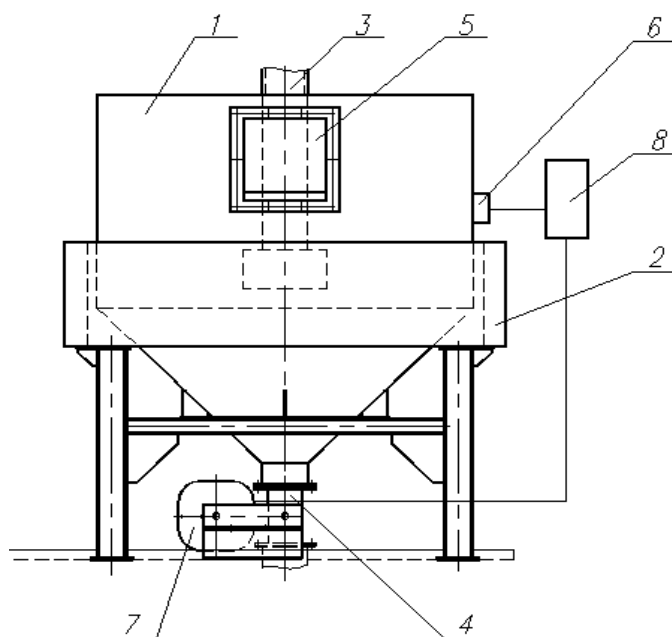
Общий вид магнитно-гравитационного сепаратора, оснащенного САКР: 1 - цилиндрический корпус; 2 - соленоидная катушка; 3 - питающая труба; 4 - разгрузочный патрубок; 5 - сливной желоб; 6 - датчик уровня ферромагнитного слоя; 7 - магнитный затвор, 8 - блок управления системы автоматической разгрузки концентрата
